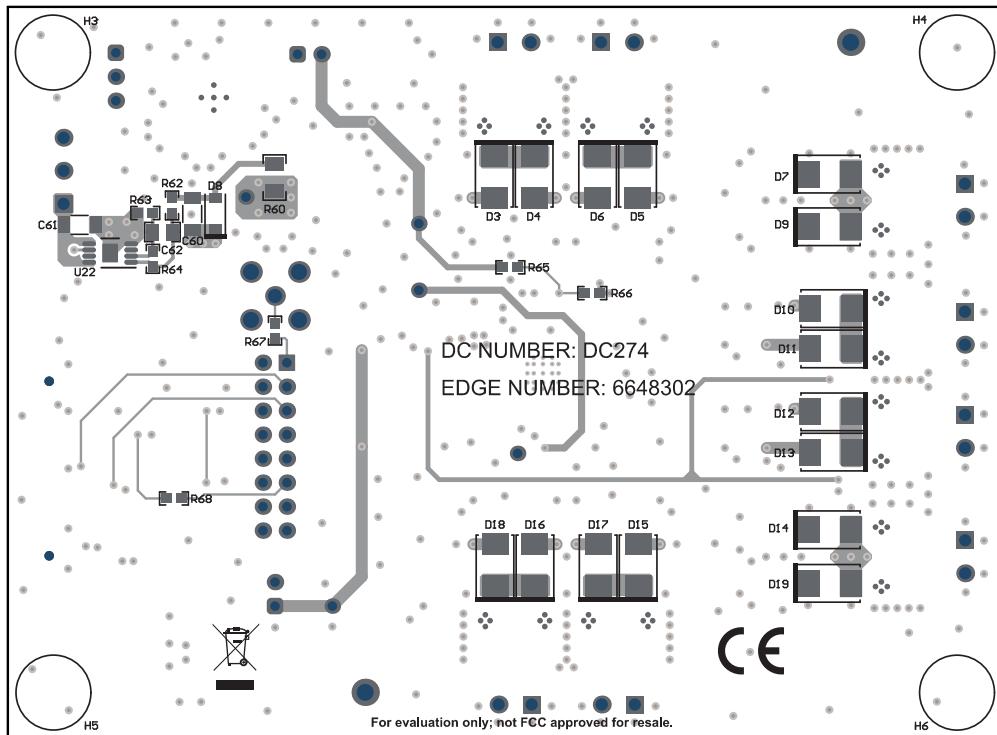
ADS125H18 評価基板 PCB レイアウト — 底面層
